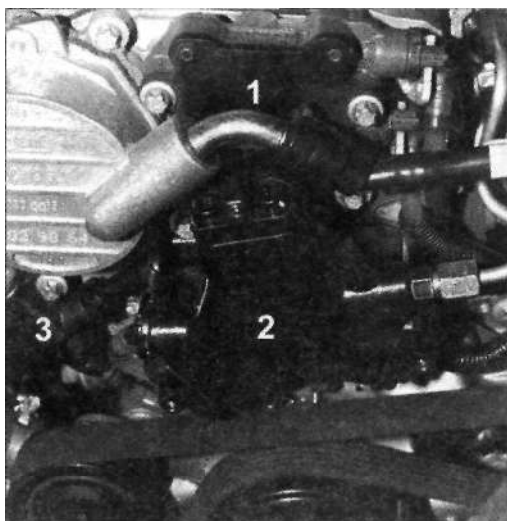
Топливные насосы двигателя Mercedes CDI: 1 — шестеренный топливоподкачивающий насос; 2 — трехплунжерный ТНВД; 3 — электромагнитный клапан останова двигателя
